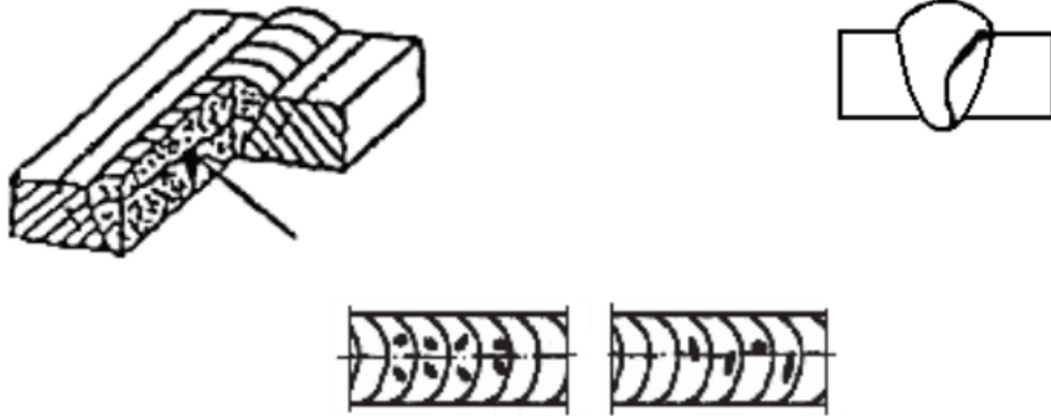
Эскиз дефекта сварного шва
